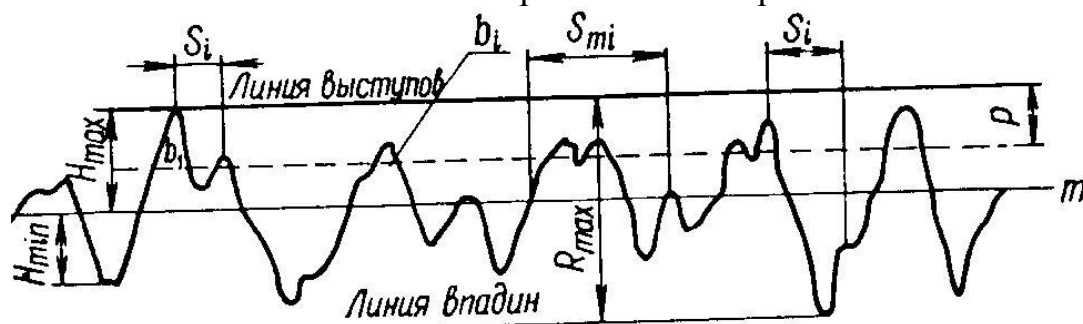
Схема для определения параметров шероховатости поверхности
